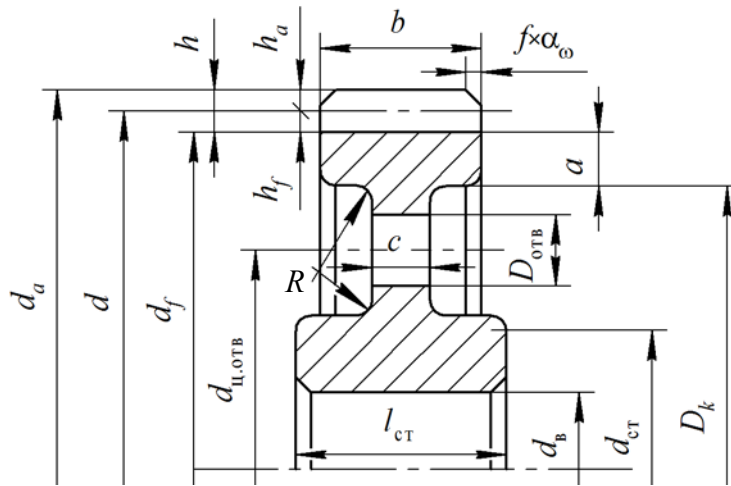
Основные параметры цилиндрических зубчатых колес
